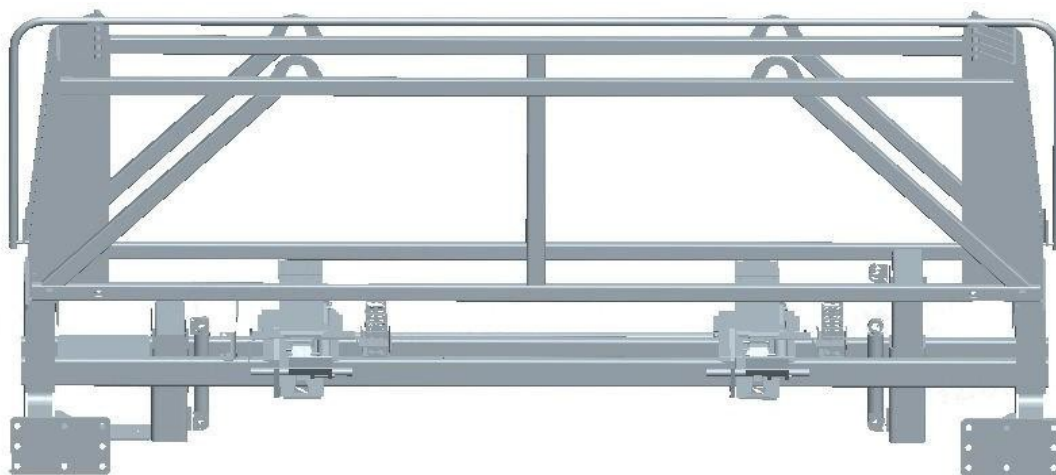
Схема устройства кассеты с автоматической загрузки и разгрузки буровых штанг
